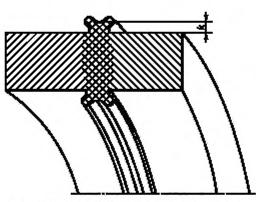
Вид валика при сварке трубы нагретым инструментом
